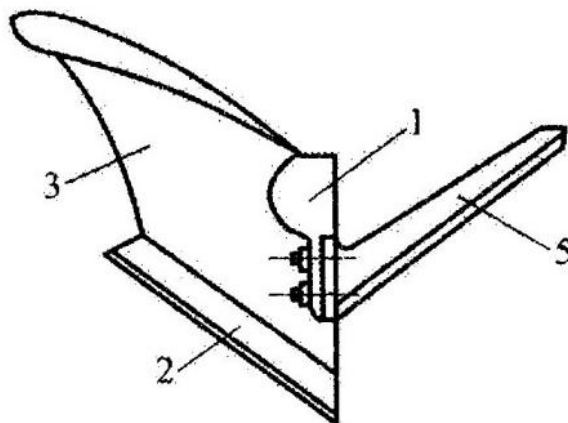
Корпус плуга, оснащений плоскорізною лапою: 1 – стояк; 2 – леміш; 3 – полиця; 5 – плоскорізна лапа.
